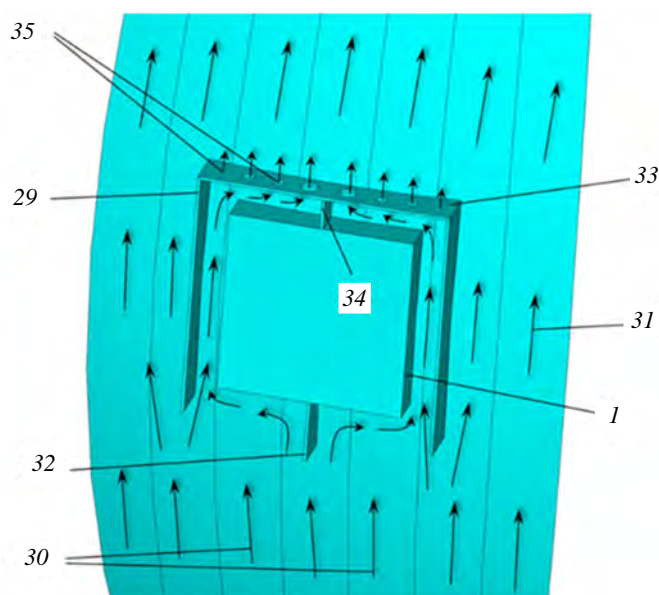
Схема установки раздаточного кожуха на корпус патрубка экваториального порта: 1 — корпус экваториального патрубка; 29 — боковые стенки раздаточного кожуха; 30 — «центральный» поток воды; 31 — «боковой» поток воды; 32 — рассекаватель; 33 — верхняя крышка раздаточного кожуха; 34 — отбойник; 35 — отверстия в верхней крышке раздаточного кожуха
